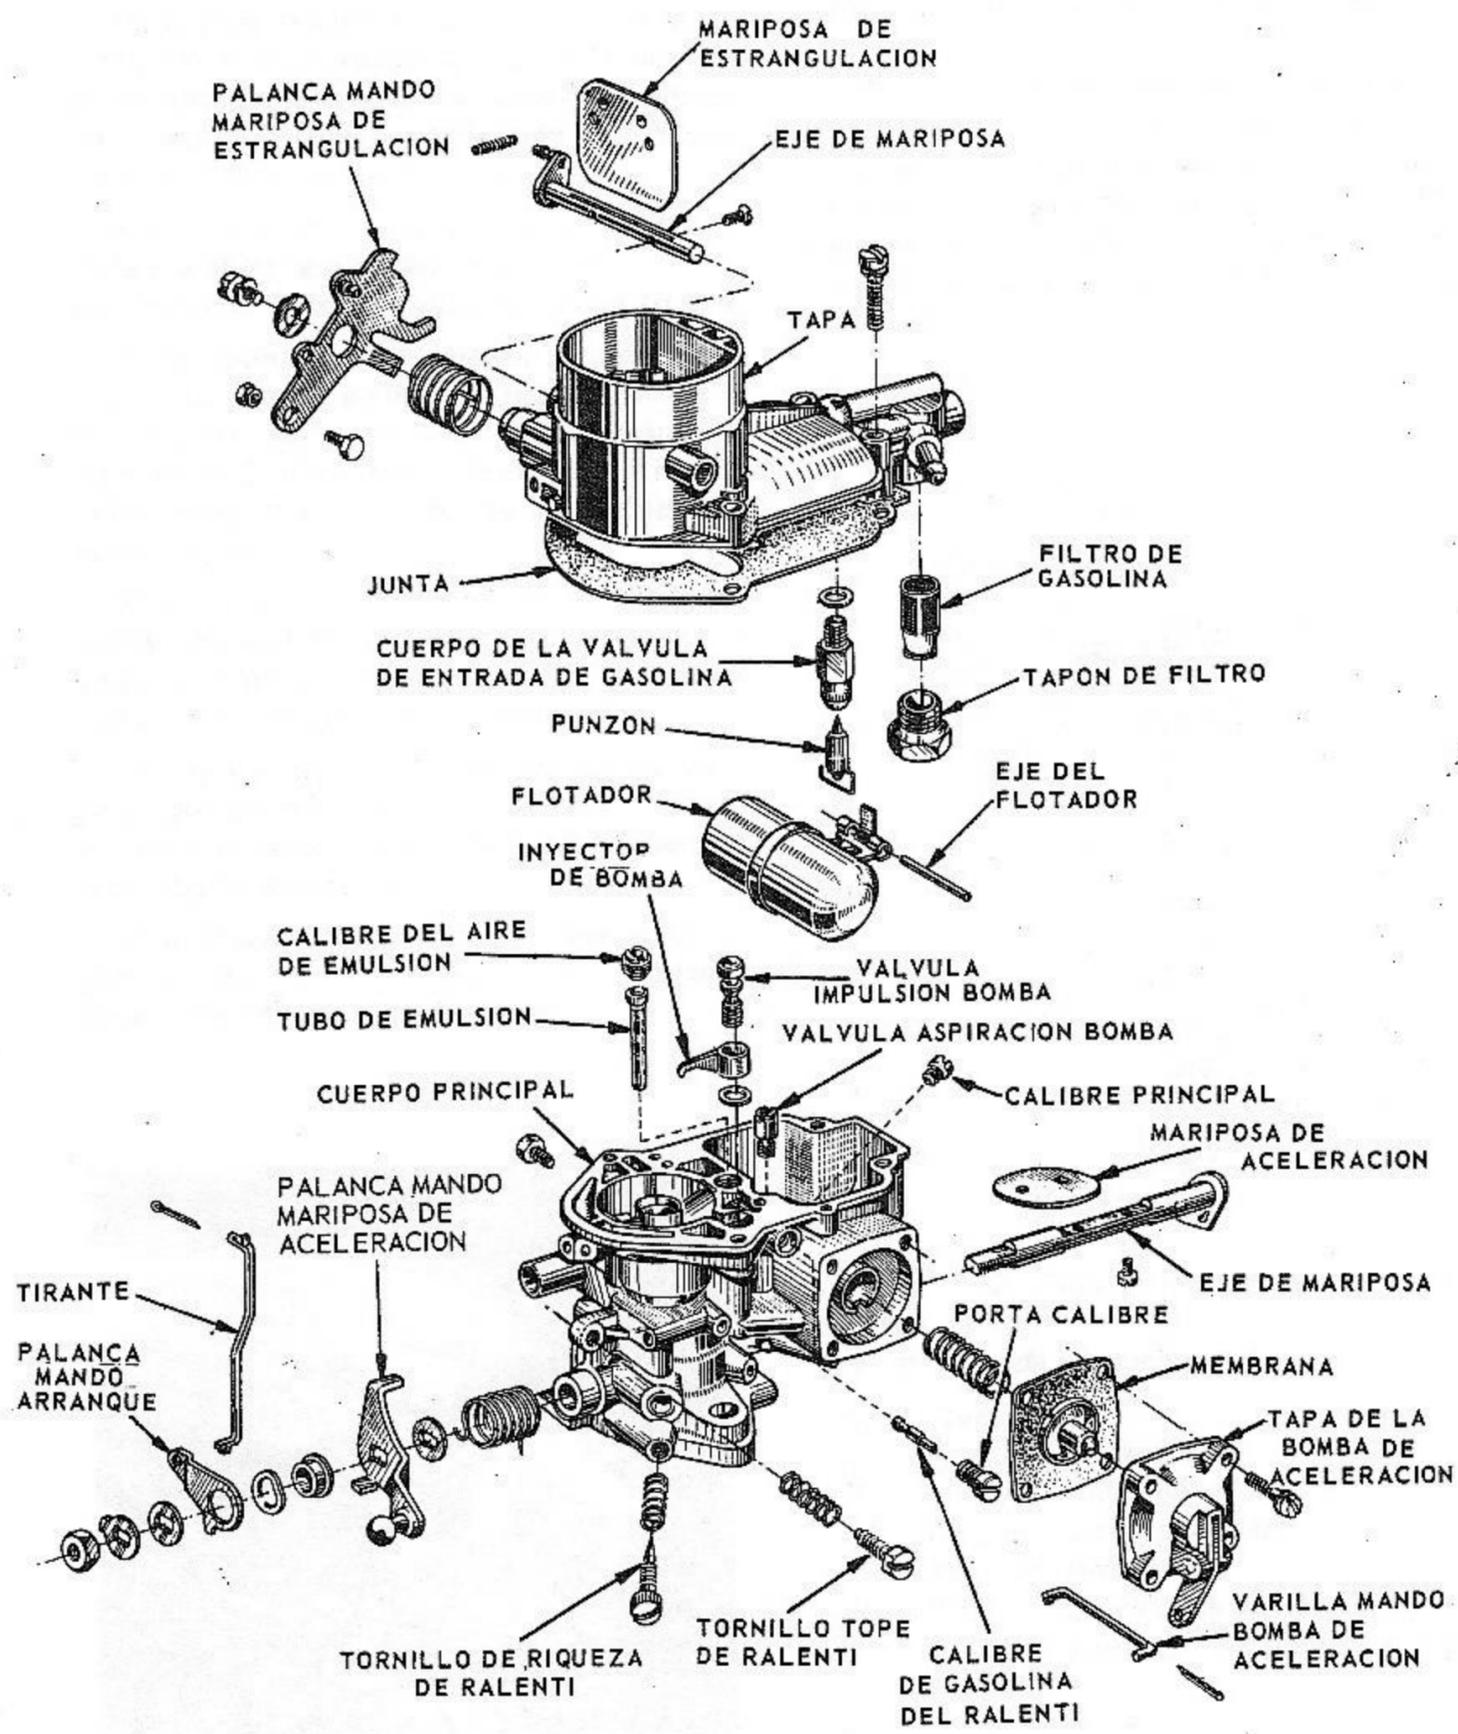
Despiece completo del carburador Weber de un solo cuerpo.
